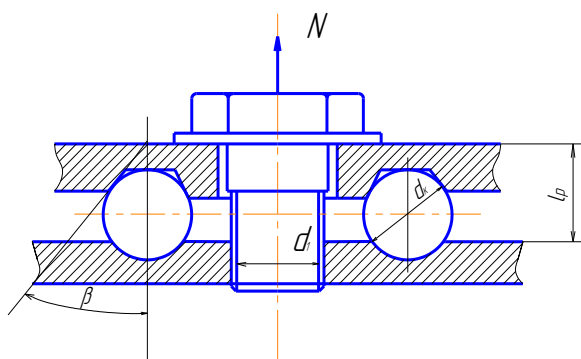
Розрахункова схема вузла кріплення каната
